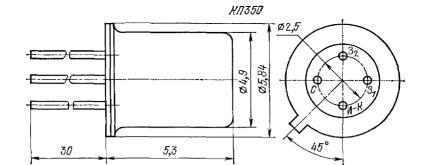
Габаритный чертеж для транзисторов КПЗ50
